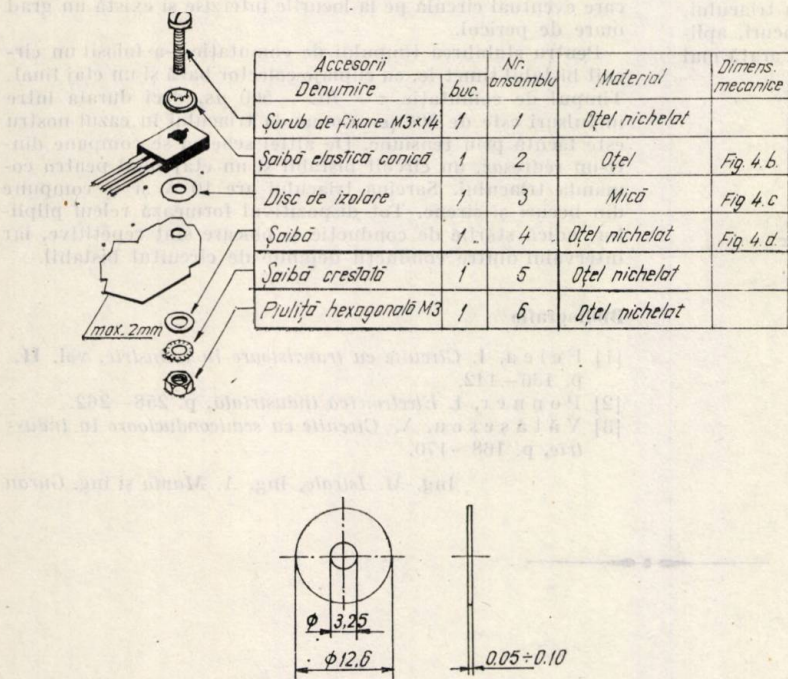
Sistem de montaj pe radiator al capsulei SOT-32 și accesoriile specifice (dimensiuni în mm):
